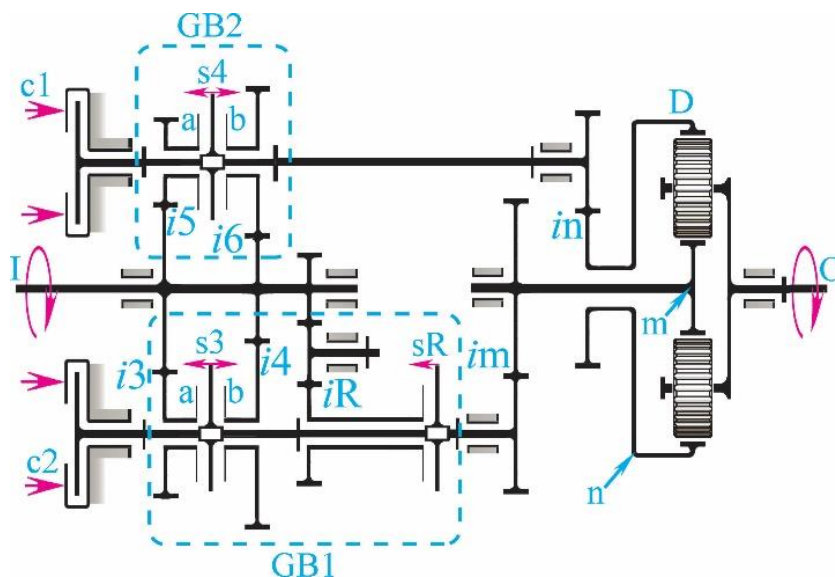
Кинематическая схема 8-ми ступенчатой двухпоточной коробки передач ID.
